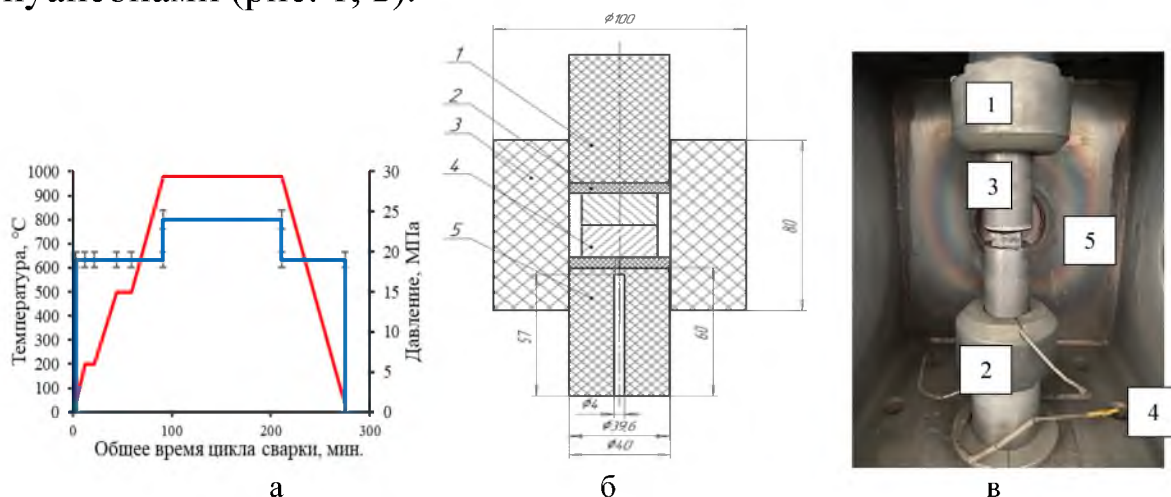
а) циклограмма диффузионной сварки на оборудовании SPS 10–3; б) схема размещения заготовок: 1 – верхний пуансон; 2 – корундовая вставка; 3 – матрица; 4 – свариваемые заготовки; 5 – нижний пуансон с технологическим отверстием под термопару; в) схема размещения заготовок перед электрической сваркой сопротивлением: 1 – гидравлический цилиндр, 2 – графитовая вставка, 3 – пуансоны, 4 – термопара, 5 – свариваемые заготовки.
